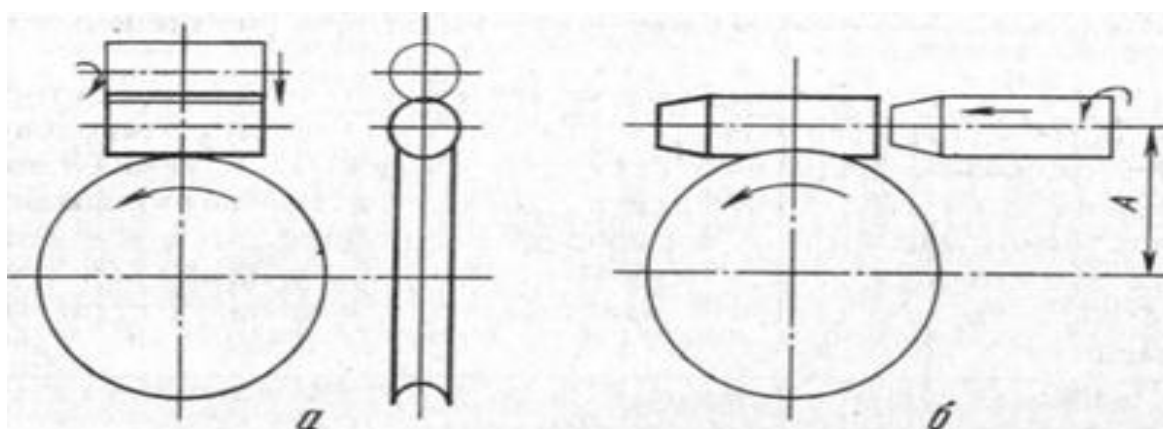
Схемы нарезания червячных колес червячной фрезой: а – с радиальным врезанием, б – с тангенциальной подачей инструмента.
